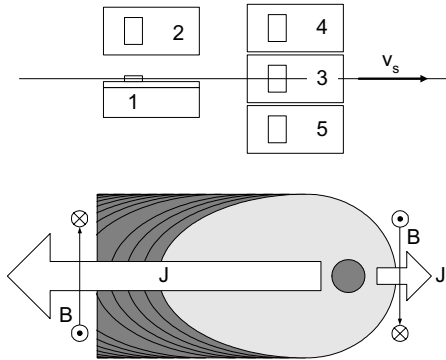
Rückschluss auf den Stromverlauf im Schweißbad (St14)
